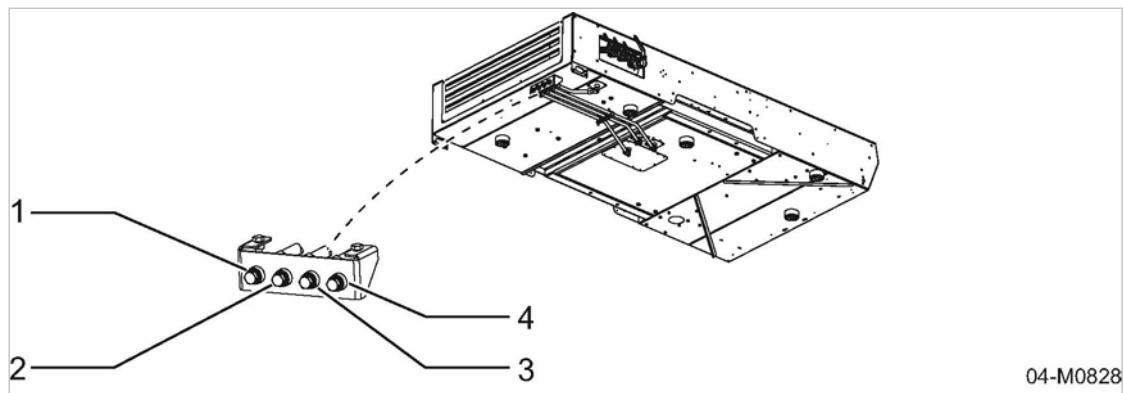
Tappested for olje og kjølevæske fra motor og kompressor
